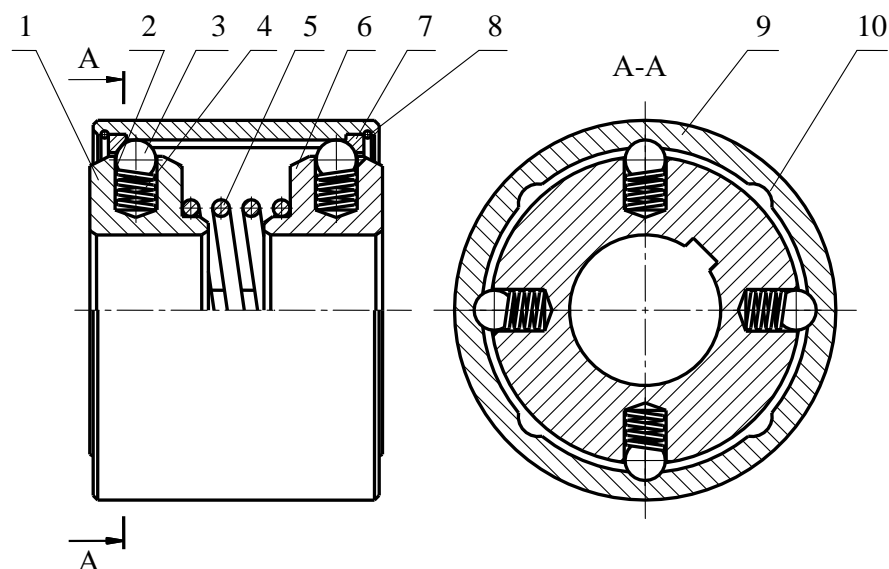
Загальна схема будови запобіжного кулькового шарнірного вузла: 1, 6 – обойма; 2 – посадковий отвір; 3 – кульки; 4 – пружини;
